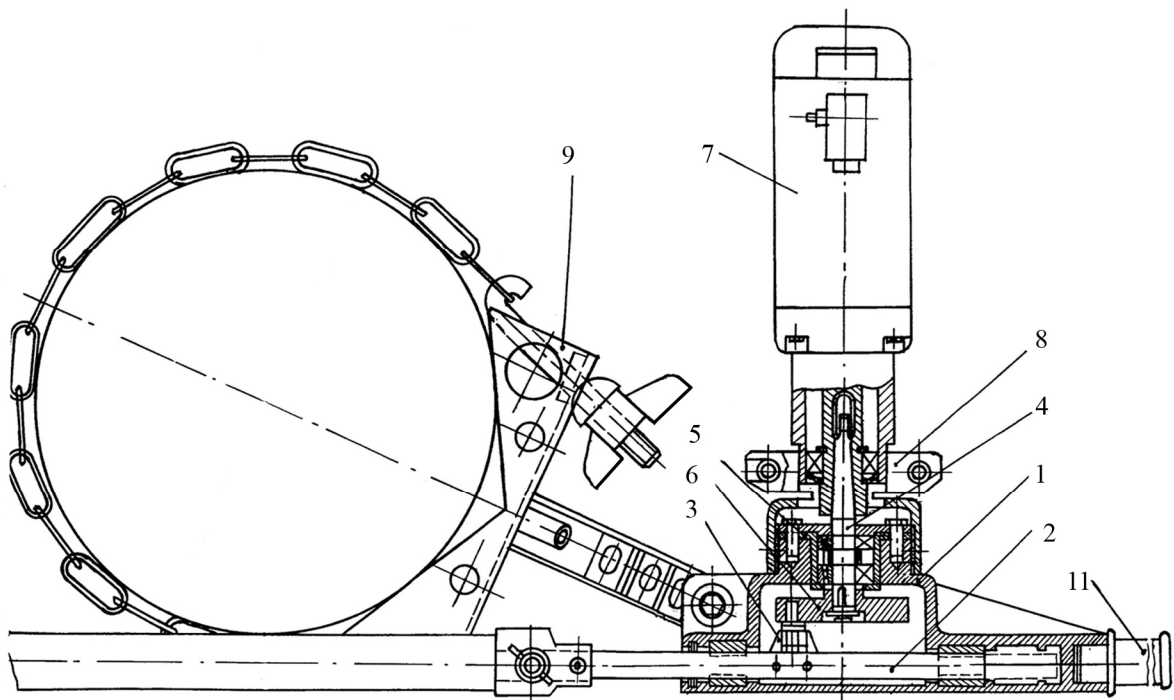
Конструкція пристрою для різання поліетиленових труб
